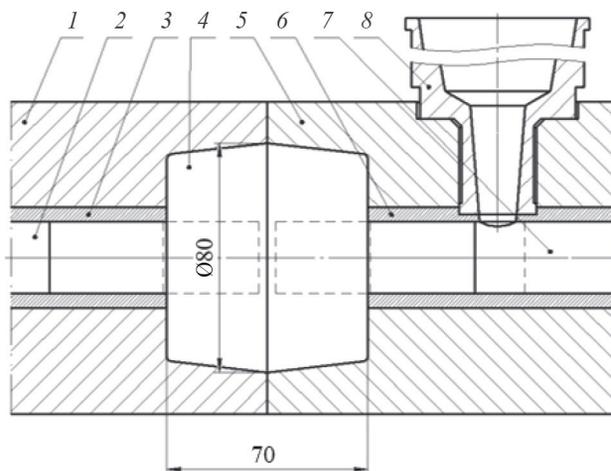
Схема процесса заливки металла и наложения давления: 1 — полуформа левая; 2 — плунжер прессующий левый; 3 — камера прессования левая; 4 — полость формы; 5 — полуформа правая; 6 — камера прессования правая; 7 — плунжер прессующий правый; 8 — чаша заливочная.
